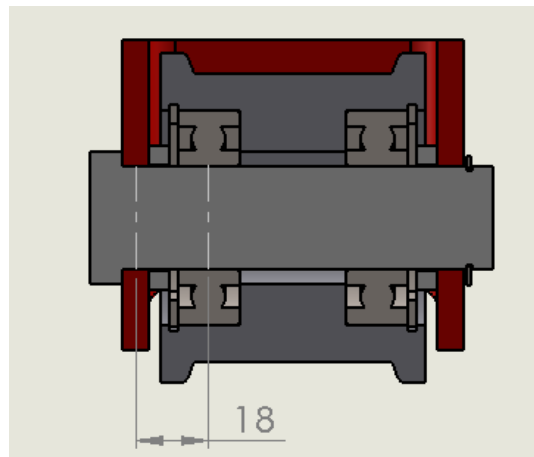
Vista en corte del ensamblaje de una rueda móvil.
